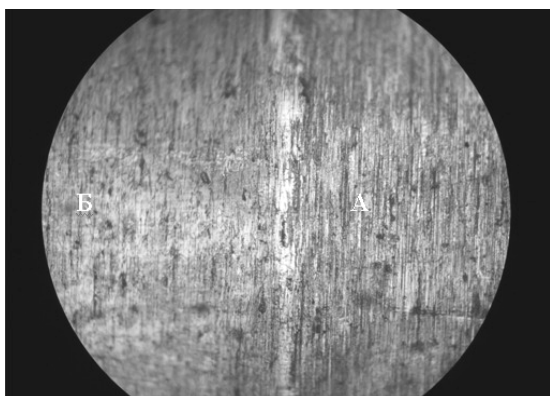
Шероховатость цилиндрического участка рабочей поверхности круглого резца; увеличение 300×:
